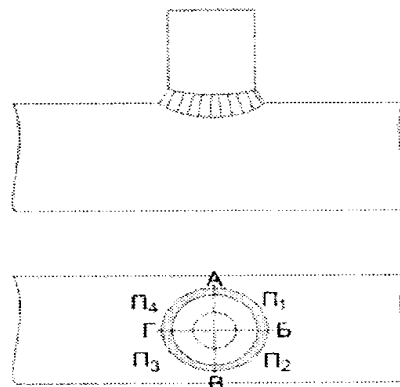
Размичування сварного соединения на сектора
